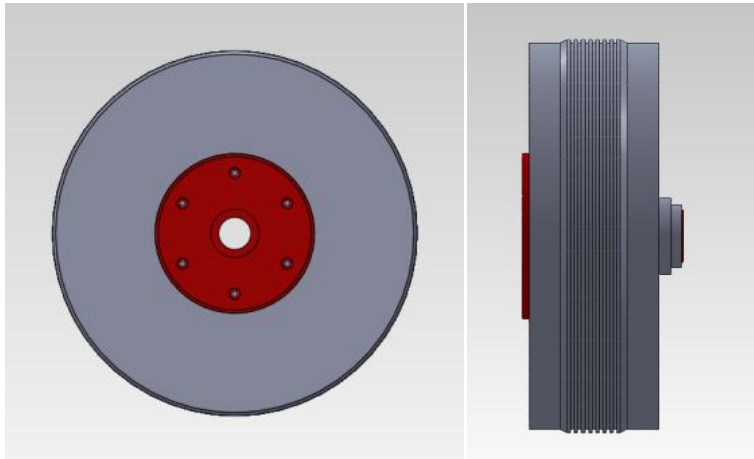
Motor de rotor externo EMRAX de 30kW
